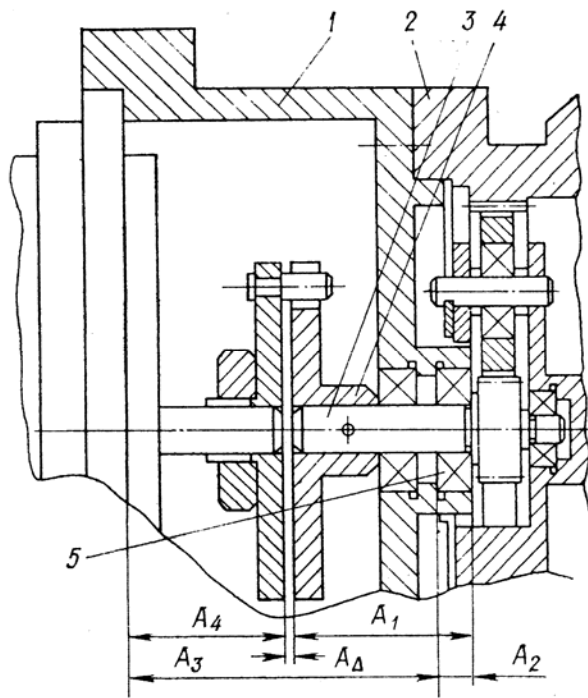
Узел подшипникового соединения: 1 – стакан; 2 – корпус; 3- вал;
